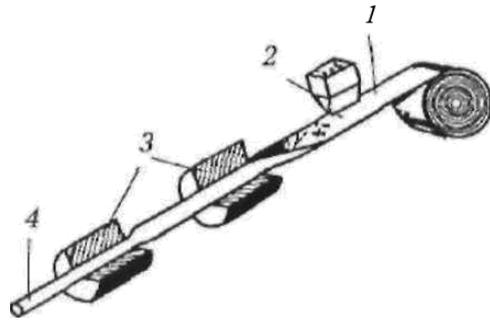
Схема изготовления порошковой проволоки:
